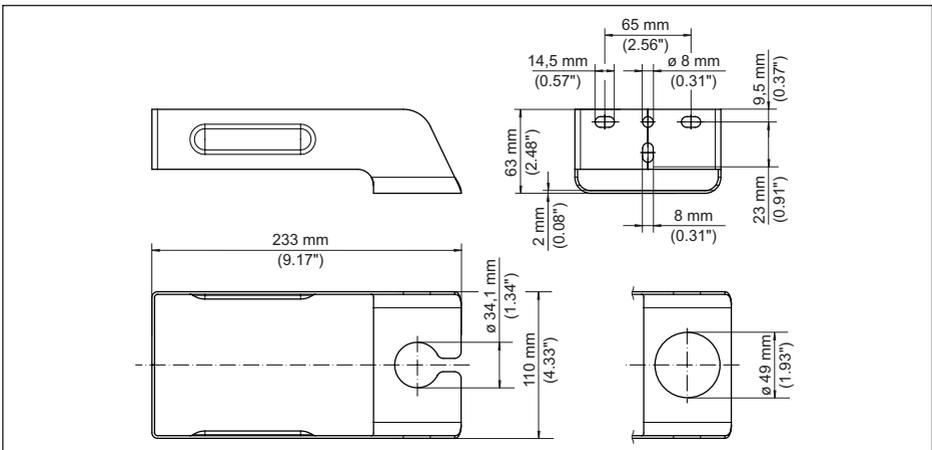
Staffa di montaggio per il montaggio a parete, fisso - braccio di supporto 200 mm
